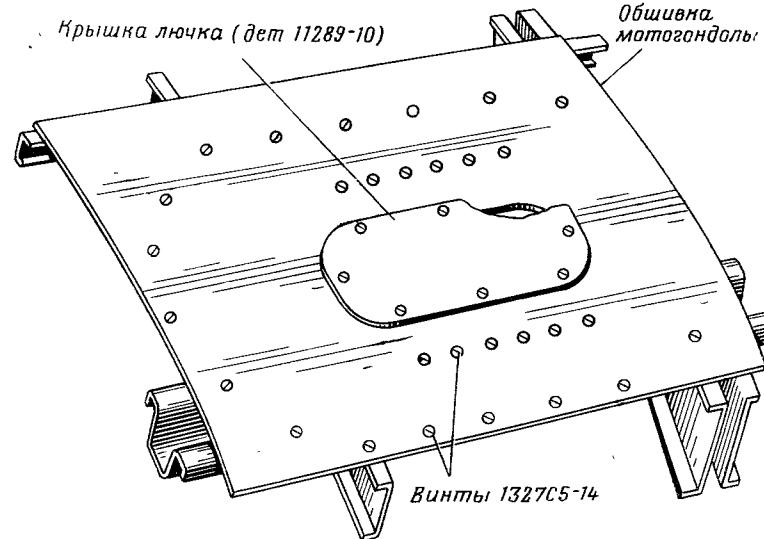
Установка крышки, закрывающей лючок в обшивке мотогондолы, сделанный для подсоединения труб к дополнительному маслорадиатору
